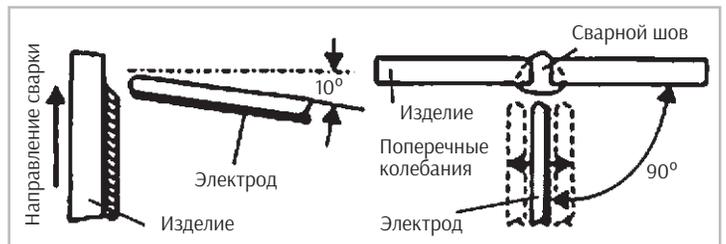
Положение электрода при сварке стыкового соединения без скоса кромок в вертикальном положении
